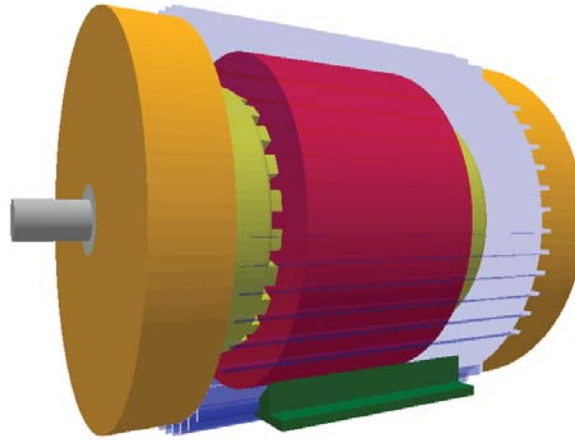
Vista 3D motor de inducción Motor-CAD
